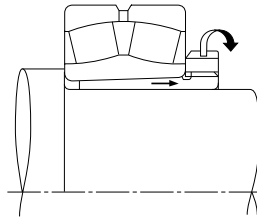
Demontage einer Abziehhülse mit Abziehmutter (1)
